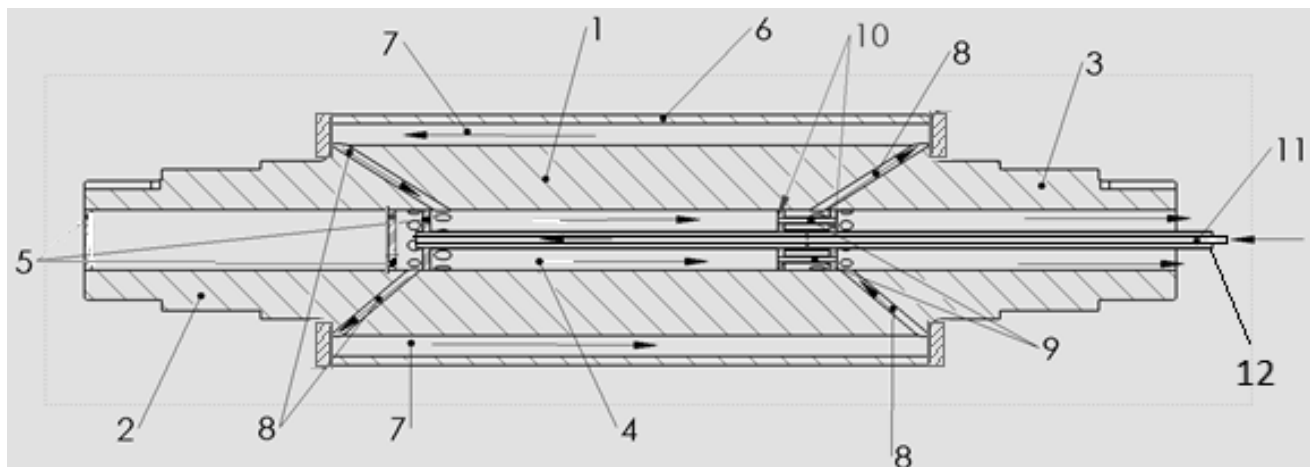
Загальний вид валка каландра в поздовжньому розрізі:
